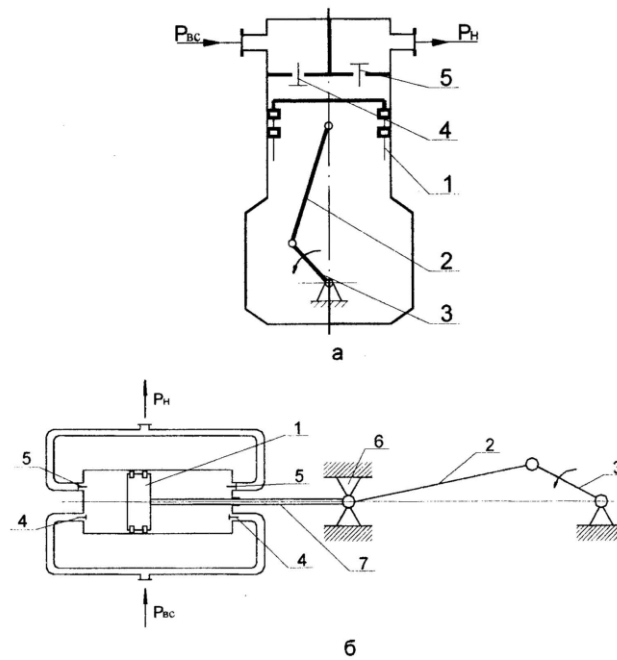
Принципиальные схемы поршневых компрессоров: а - одностороннего действия; б - двухстороннего действия; 1 - поршень с кольцами; 2 - шатун; 3 - кривошип; 4, 5 - всасывающий и нагнетательный клапаны; 6 - крейцкопф; 7 - шток
